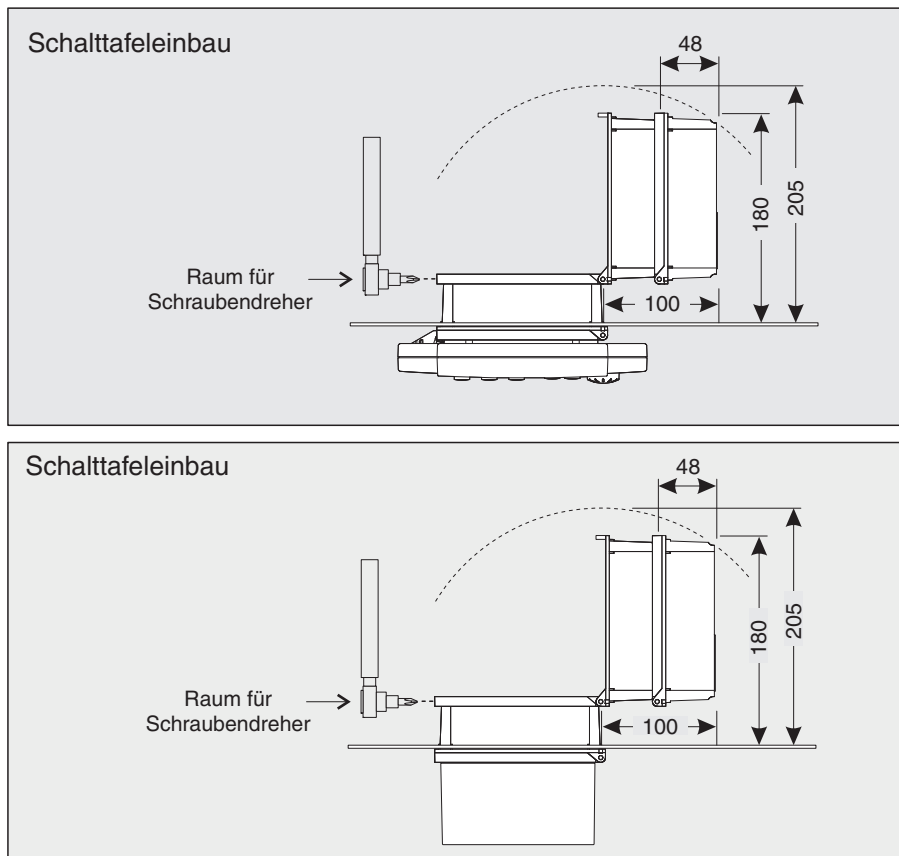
Raumbedarf für Schalttafeleinbau (Maße in mm)
